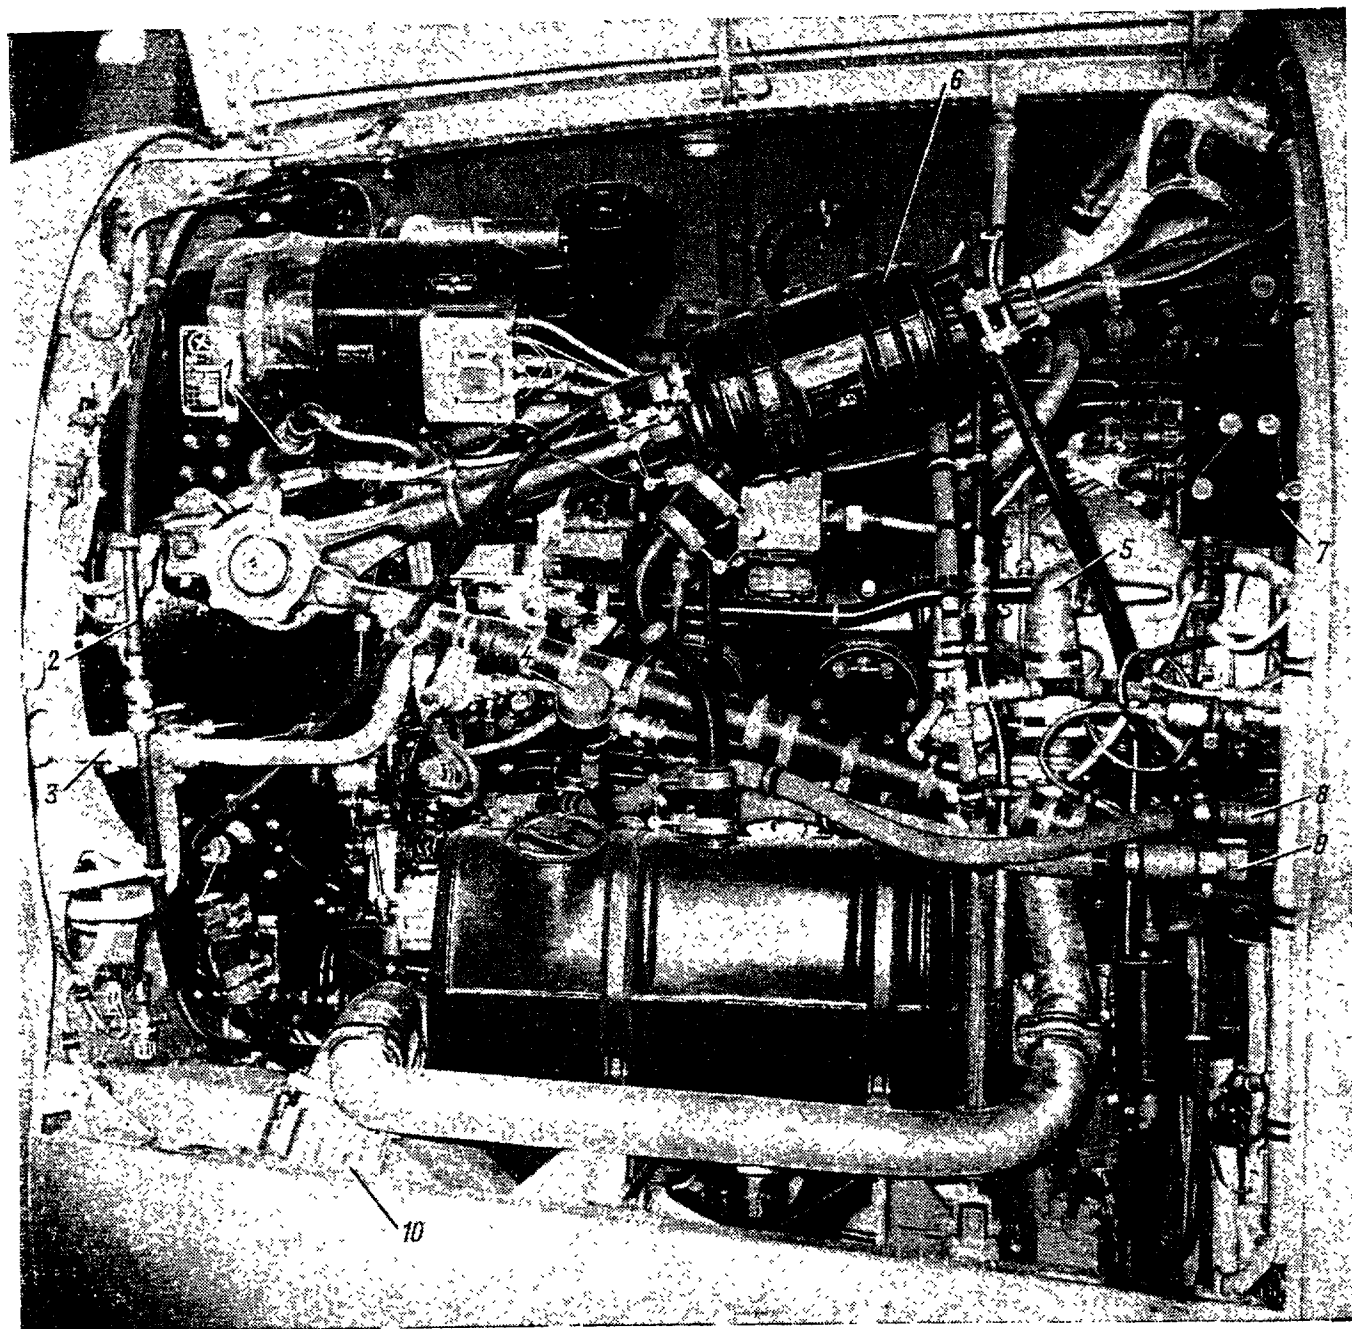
Установка левого двигателя. На правом борту гондолы виден воздухозаборник обдува горячих частей двигателя
